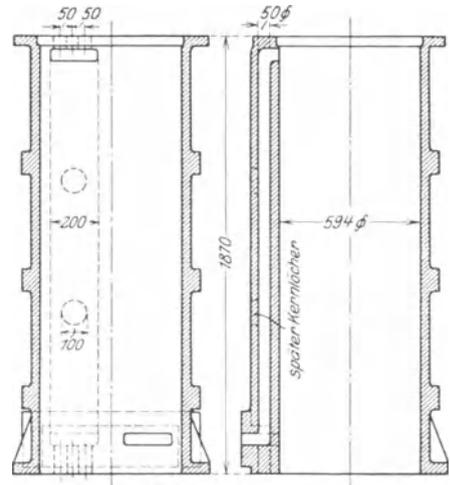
Dampfzylinder zu einem 3000-kg-Hammer.
